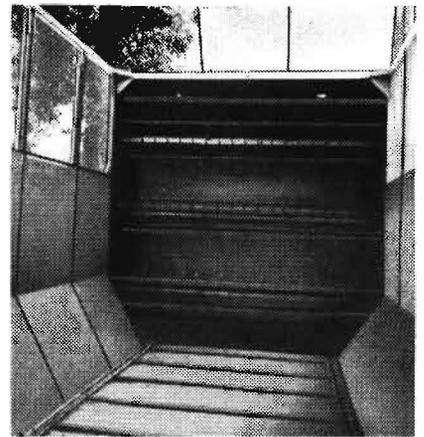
Die Fräseinrichtung des Einachsanhängers NTV-2,5 in der Ausführung als Großraumfahrzeug
